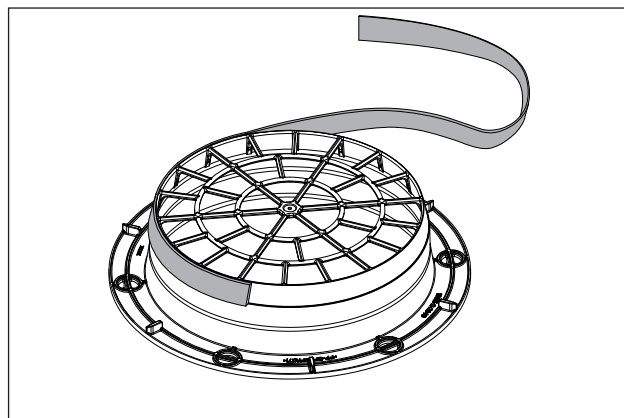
Position på forseglingsstapen til montering med rundrør
